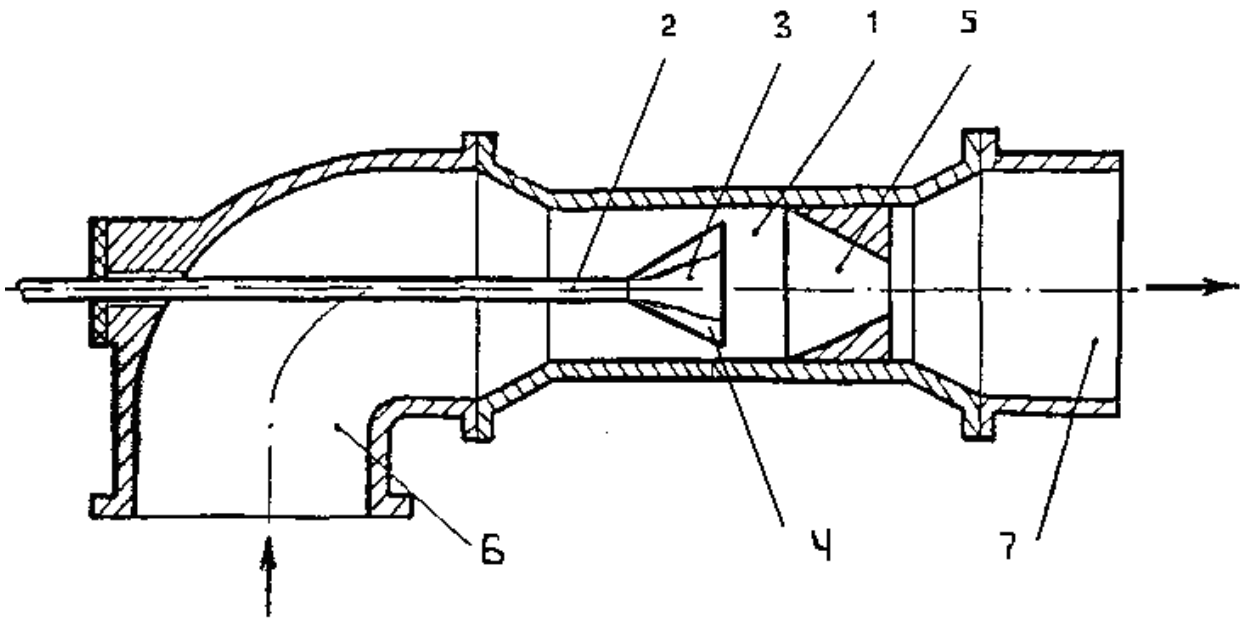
Гідродинамічний кавітатор статичного типу: 1- проточна камера; 2- шток; 3- кавітатор; 4- конічний насадок; 5- дифузор; 6- конфузор; 7- патрубок відведення середовища.
